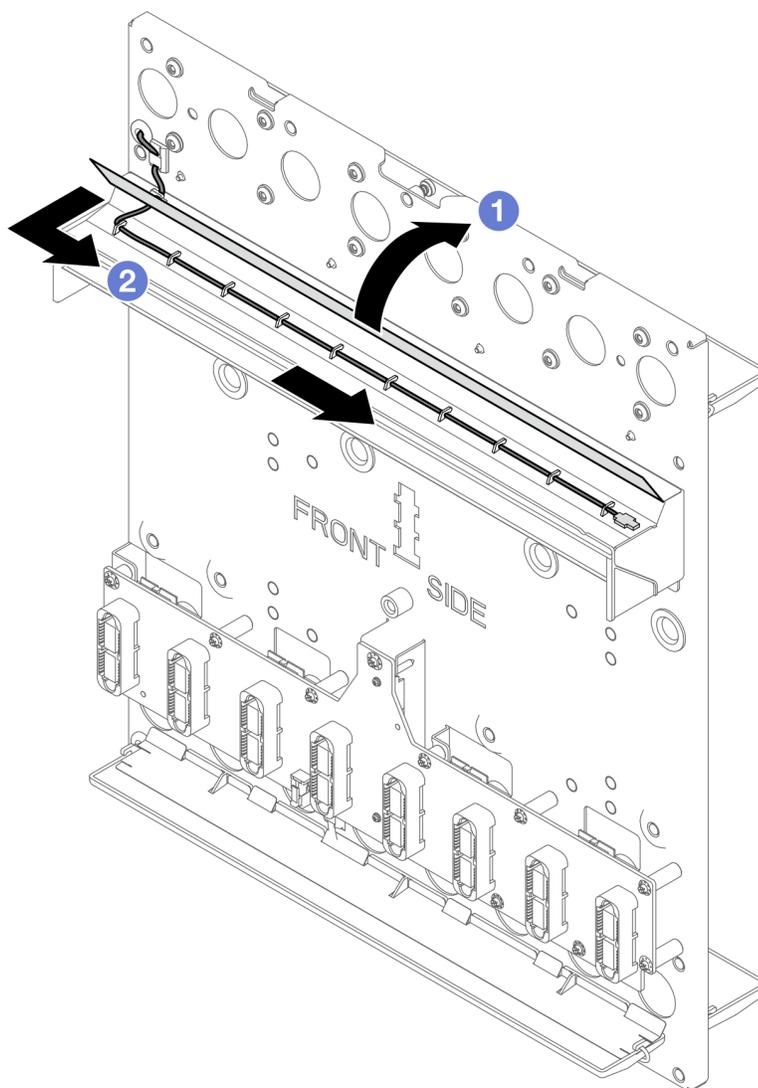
Fixation du câble du détecteur de fuite au bac d'égouttage supérieur sur la face avant
